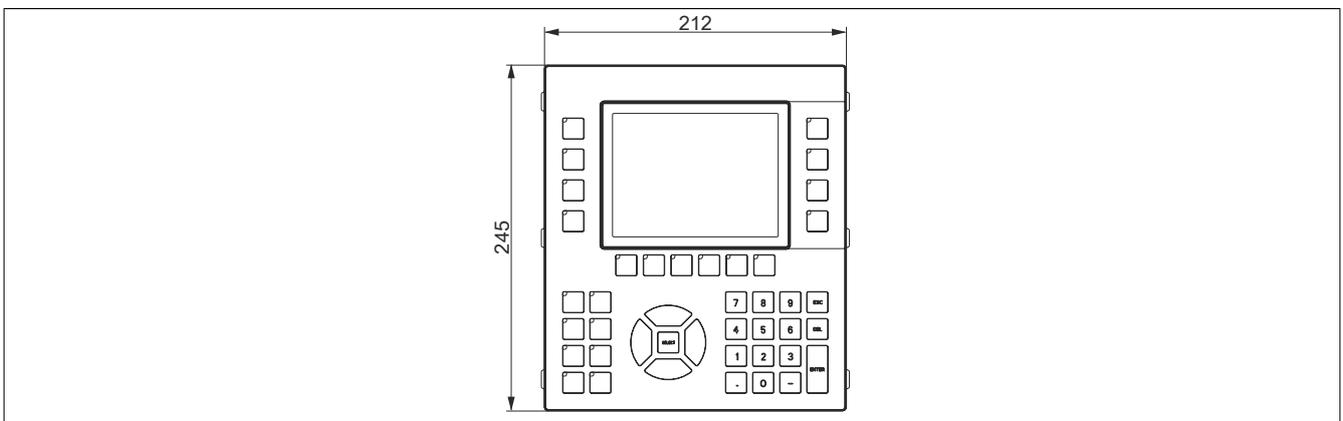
5AP1151.0573-000 - Abmessungen
